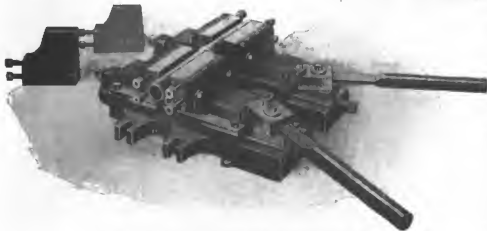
Klemmvorrichtung für Röhrenschweissung.
